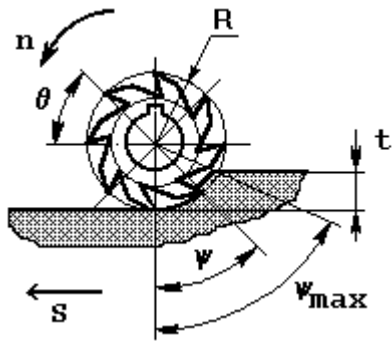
Схема определения условий равномерного фрезерования прямозубой цилиндрической фрезой
